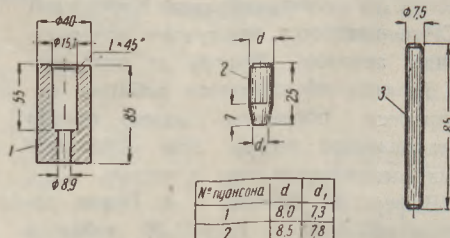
Приспособление и инструмент для раздачи витого ролика подшипника задней ступицы:
